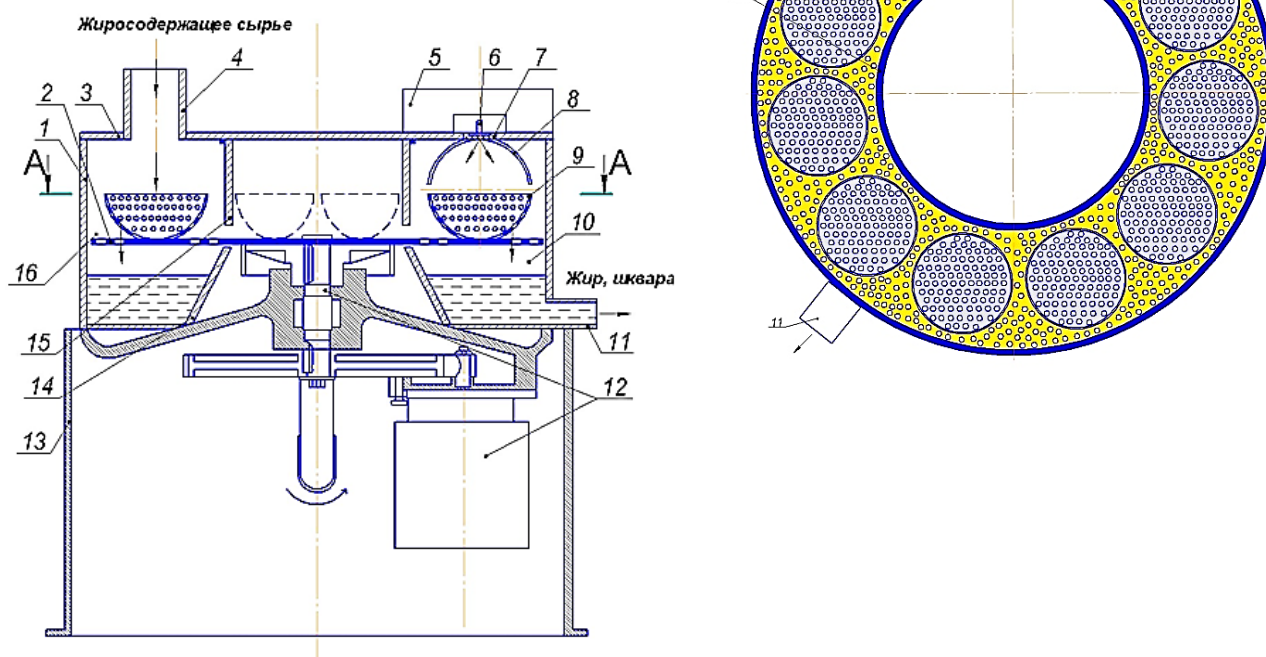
Центробежная установка для термообработки жиросодержащего сырья в ЭМПСВЧ: 1 – экранирующий цилиндрический корпус; 2 – перфорированный диск-ротор; 3 – крышка экранирующего корпуса со смотровым окном; 4 – приемный патрубок; 5 – СВЧ генераторные блоки; 6 – излучатель; 7 – диэлектрическая втулка; 8 – верхние (стационарные) полусферы резонаторных камер; 9 – нижние (передвижные) перфорированные полусферы резонаторных камер; 10 – поддон; 11 – выпускной патрубок; 12 – электродвигатель с передаточными механизмами; 13 – станина; 14 – усеченный конус; 15 – цилиндр; 16 – тороидальный волновод.
